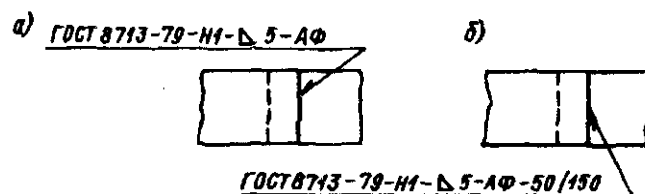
Обозначение длины сварных швов: а — сплошных; б — прерывистых
